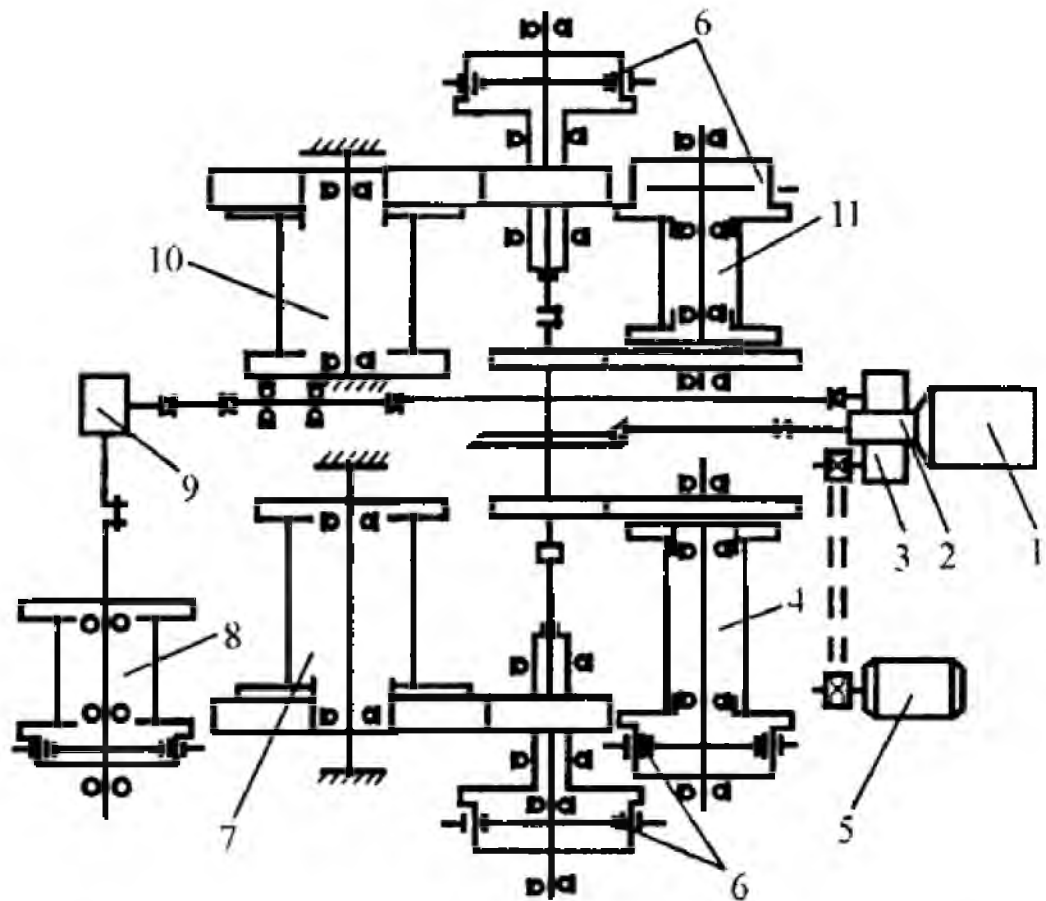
Кінематична схема несамохідної лебідки ЛД-8. 1 - двигун; 2 - коробка передач; 3 - коробка відбору потужності; 4 - основний поворотний барабан; 5 - генератор струму; 6 - пневмокамерні муфти; 7 - основний вантажний барабан; 8 - допсміжний приставний барабан; 9 - редуктор; 10 - вантажний допсміжний барабан; 11 - поворотний допсміжний барабан
